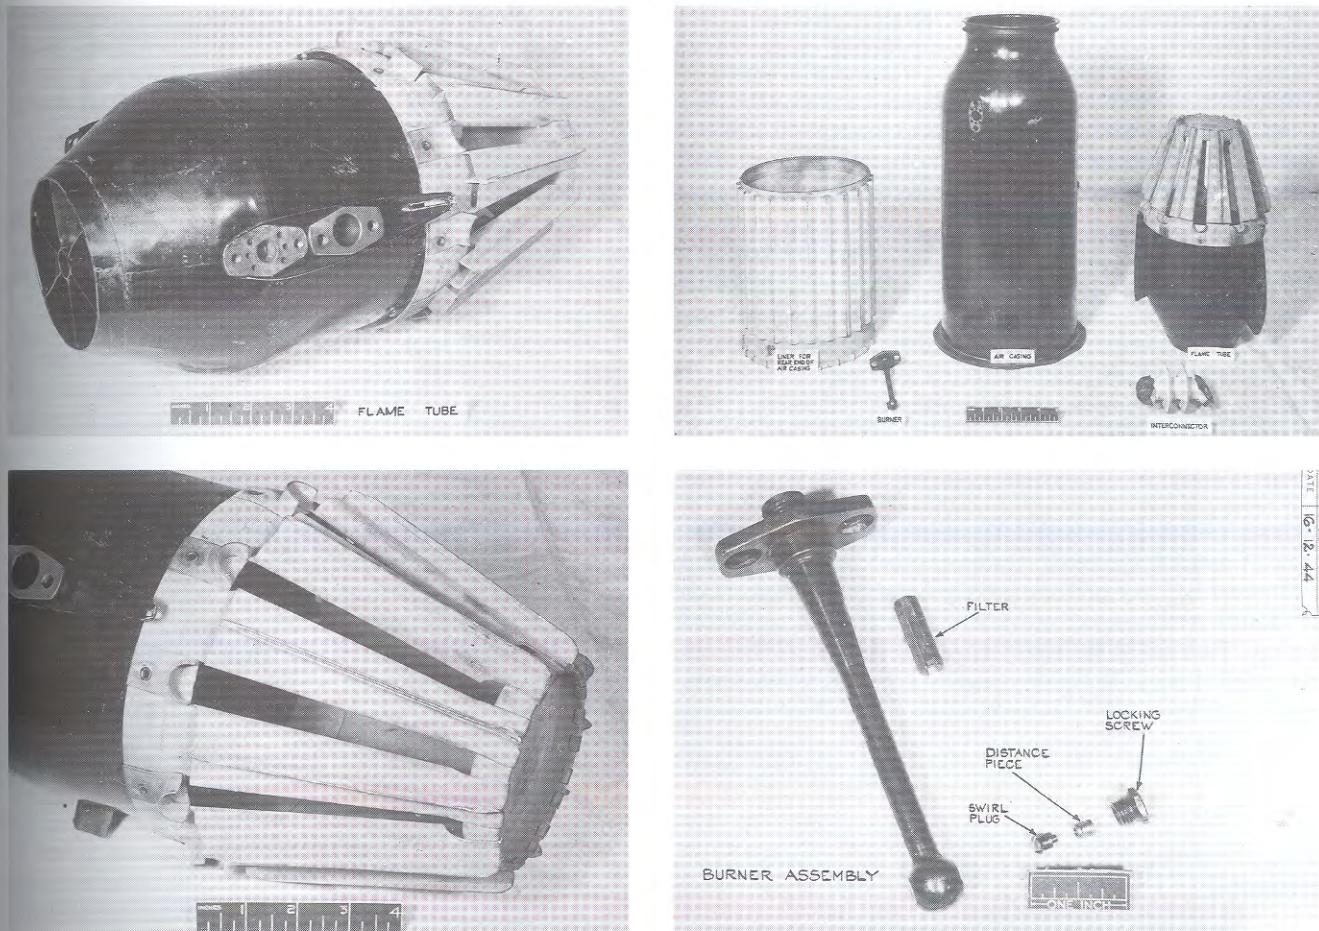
Элементы одной из камер сгорания турбореактивного двигателя Юнкерс 109-004 В-1
